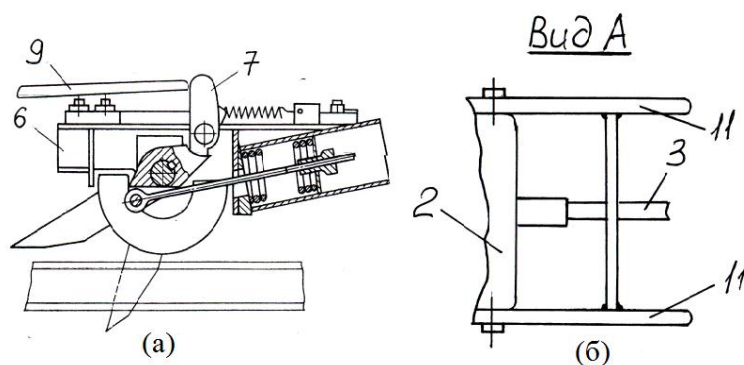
Конструктивная схема тормозной системы устройства (а), продольный разрез и вид А (вид сверху) (б) на рис. 1
